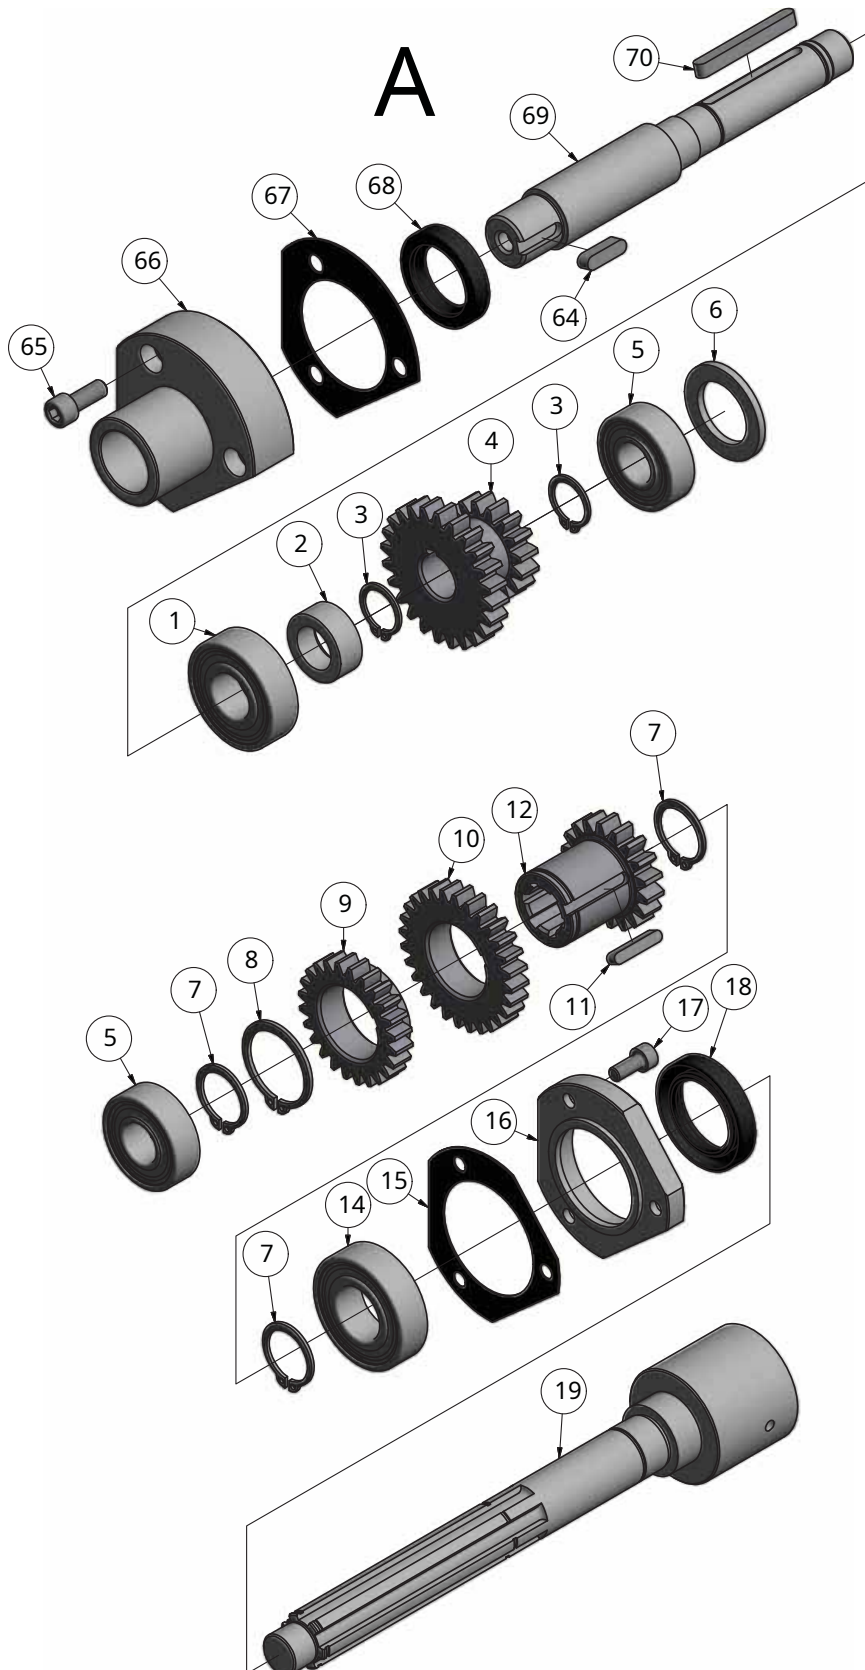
Vorschubgetriebe 3-6 - Engranaje de alimentación 3-6
